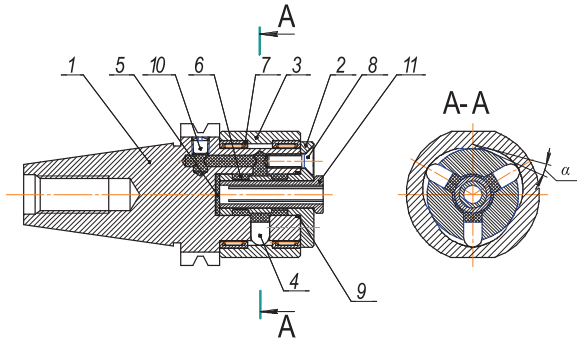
Конструктивна схема інструментального затискного патрона з гідропластом: 1 – корпус, 2 – циліндрична тонкостінна втулка, 3 – поворотна обойма, 4 – плунжер, 5 – фторопластова шайба, 6 – плинне середовище – гідропласт, 7 – голчастий підшипник, 8 – гвинт, 9 – фторонітова прокладка, 10 – пробка, 11 – цанга
